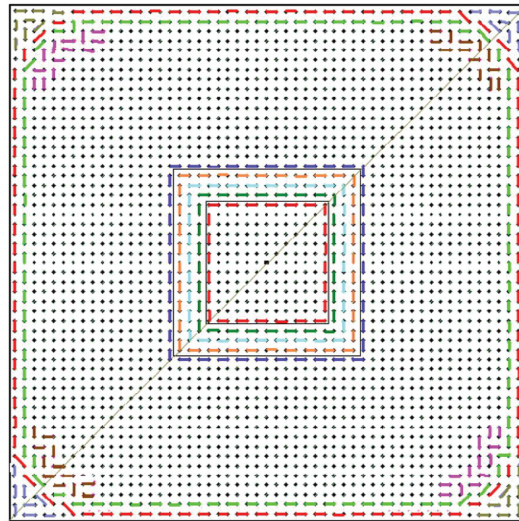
Connexions en guirlandes des joints de soudure [11]
